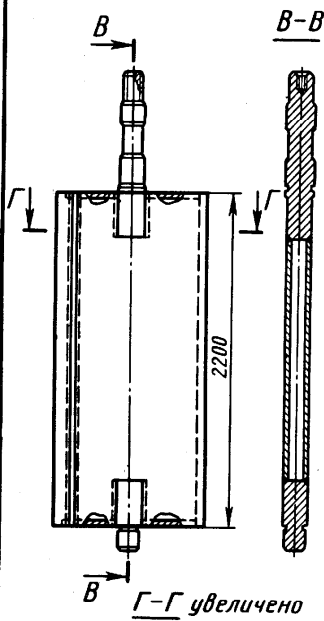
Сварная лопатка направляющего аппарата
